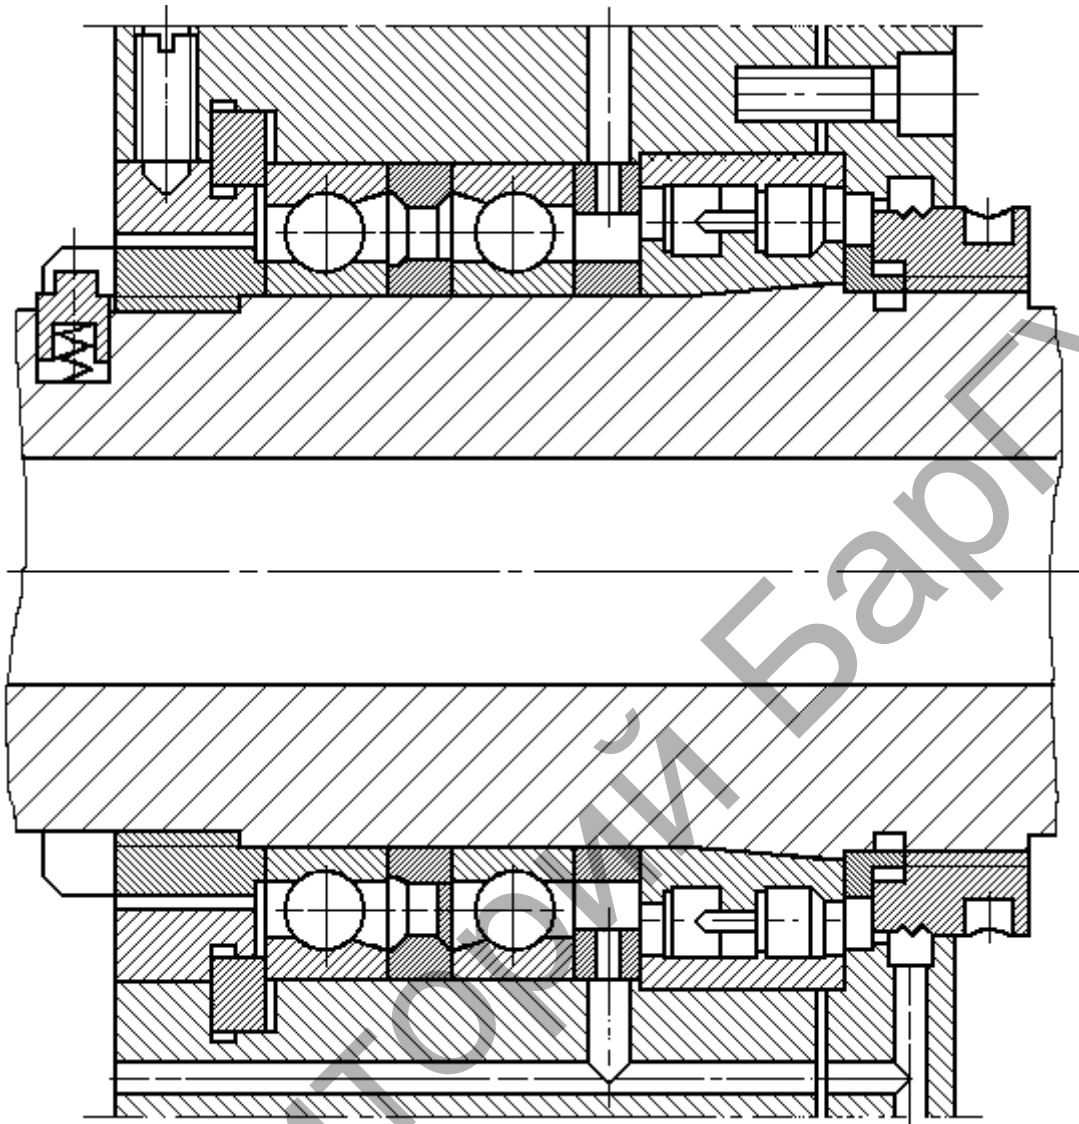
Передняя опора шпинделя расточного станка с тремя подшипниками
